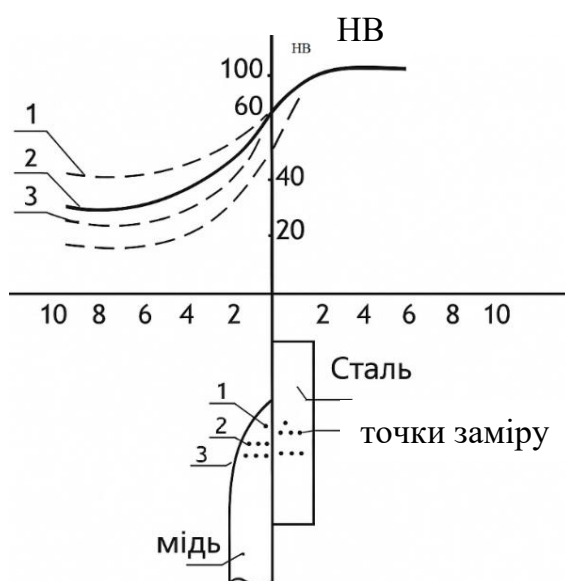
Схема замірів твердості металу зони зварного з'єднання
